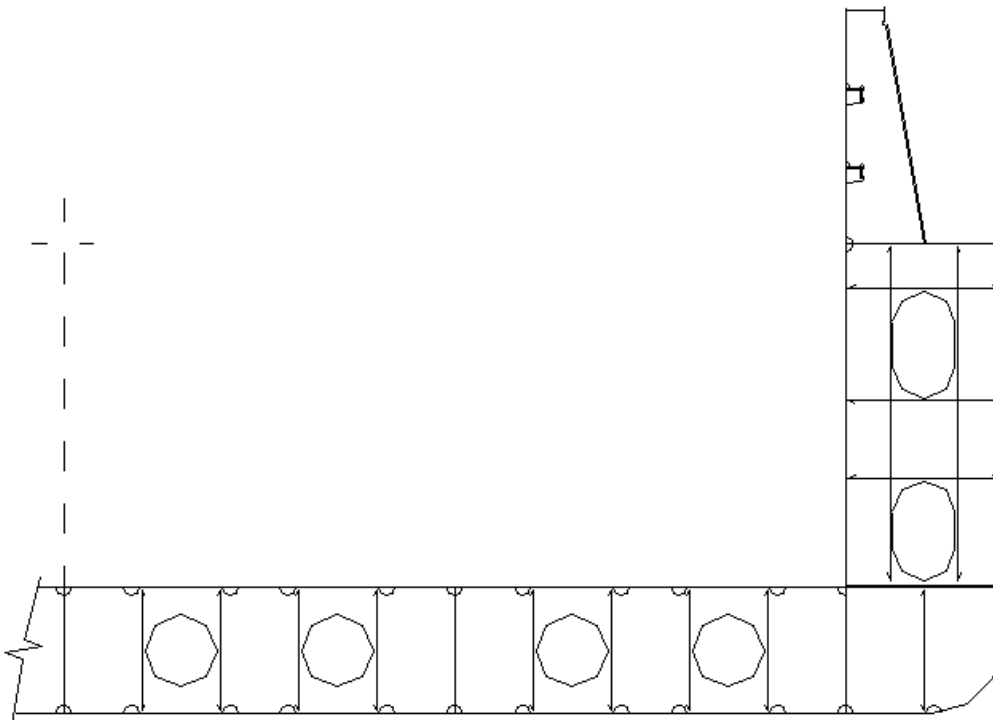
SISTEMA LONGITUDINAL – CAVERNA
